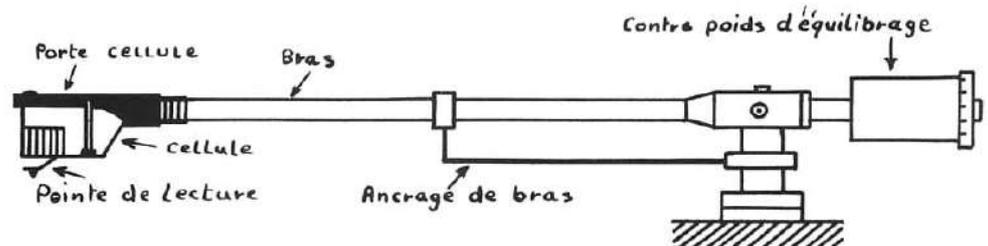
ENSEMBLE BRAS/TETE DE LECTURE.
